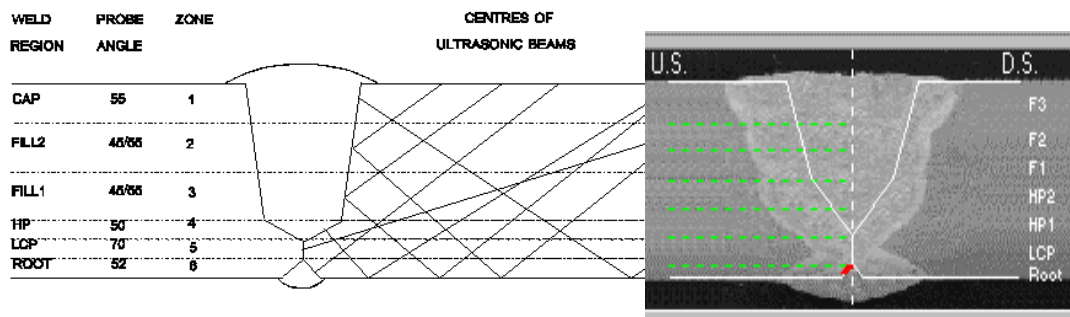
MAPEO DEL CORDON DE SOLDADURA
